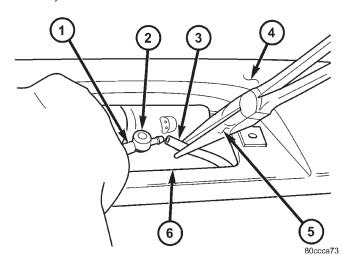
Desmontaje e instalación de la válvula de retención trasera
